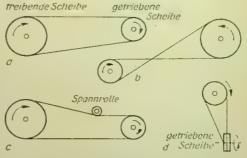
Riementriebe: a offen. b gekreuzt. c mit Spannrolle, d Winkeltrieb
